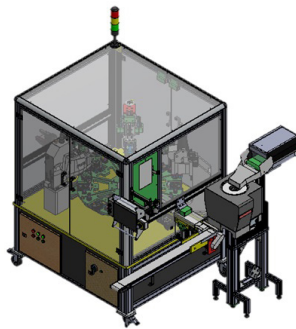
Prototipo de nueva máquina robot remachadora rotary.
